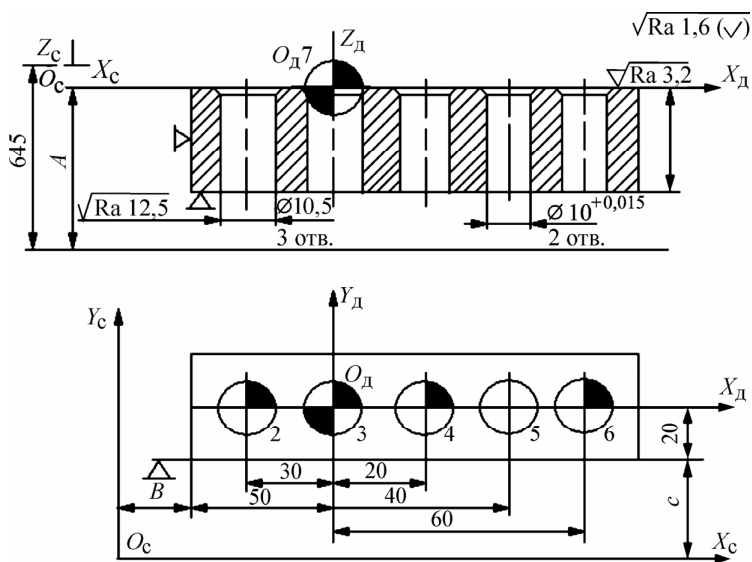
Система координат деталей, обрабатываемых на многоцелевом станке
